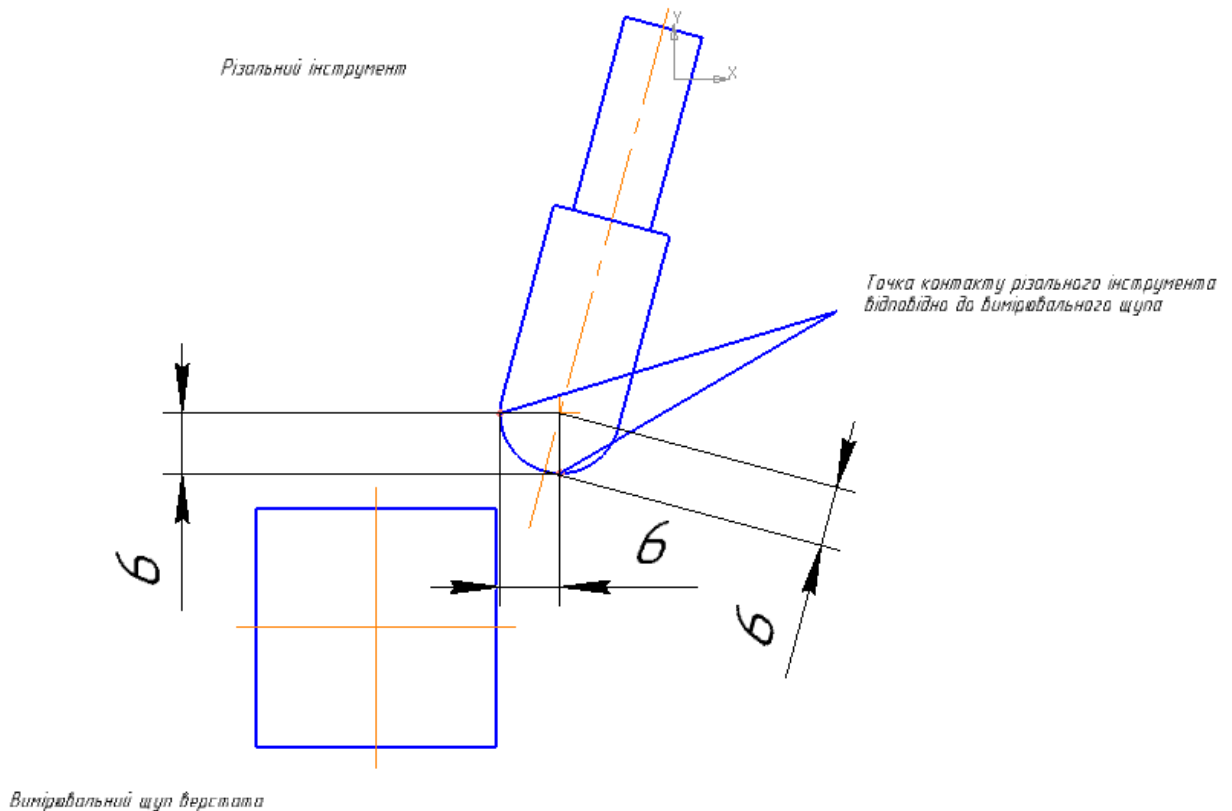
Схема визначення точки позиціювання різального інструмента завдяки інструменту «Напівсфера»
